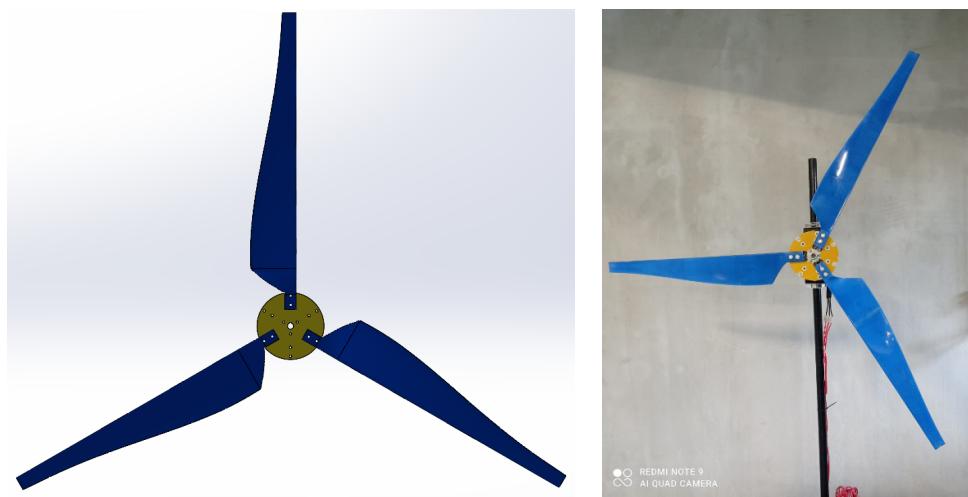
Diseño del rotor (izquierda) y rotor manufacturado (derecha). Fuente: los autores.
